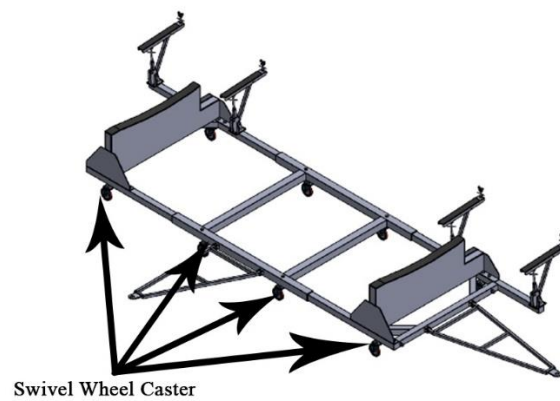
Dimensi Towbar dari Center Wing Cradle
